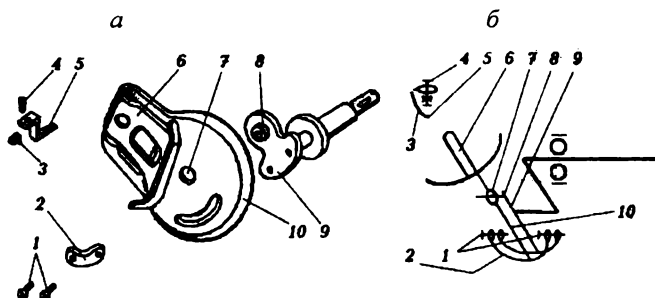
Нитепритягиватель машины 97-А кл. ОЗЛМ:
